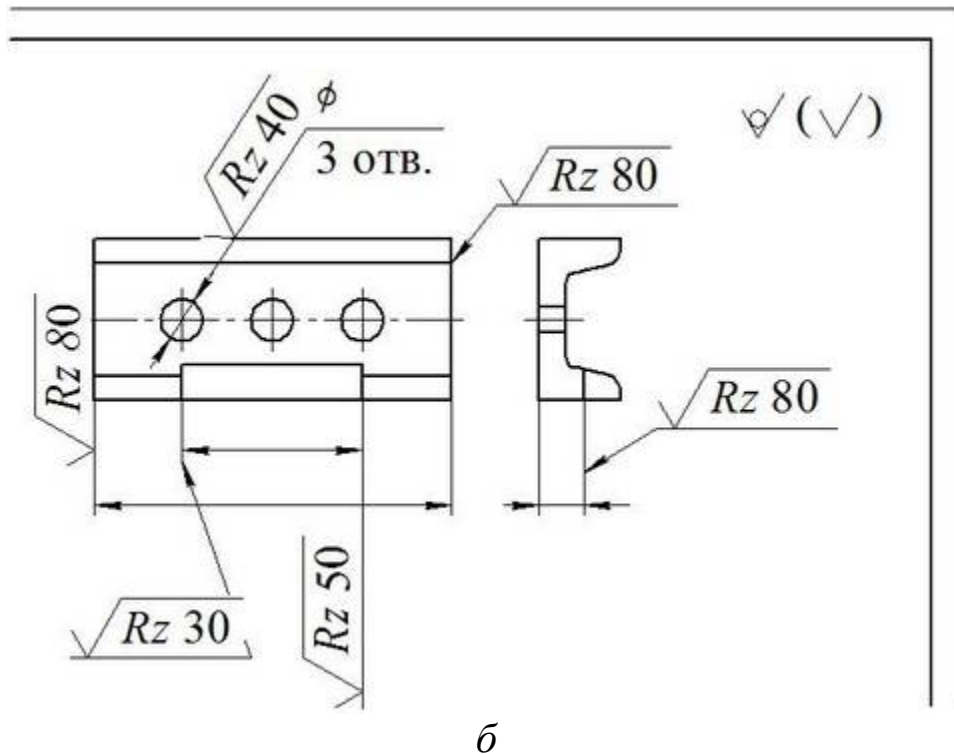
Схема расположения обозначения шероховатости в правом верхнем углу чертежа
